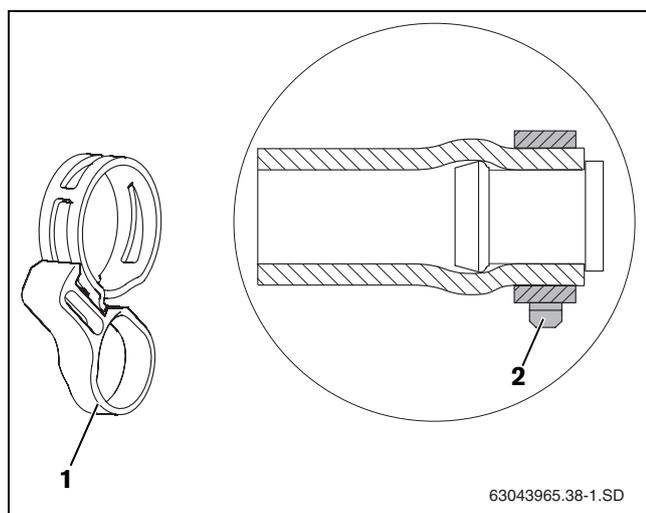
Fascetta stringitubo con anello di sicurezza dopo il montaggio al tappo cieco premontato
